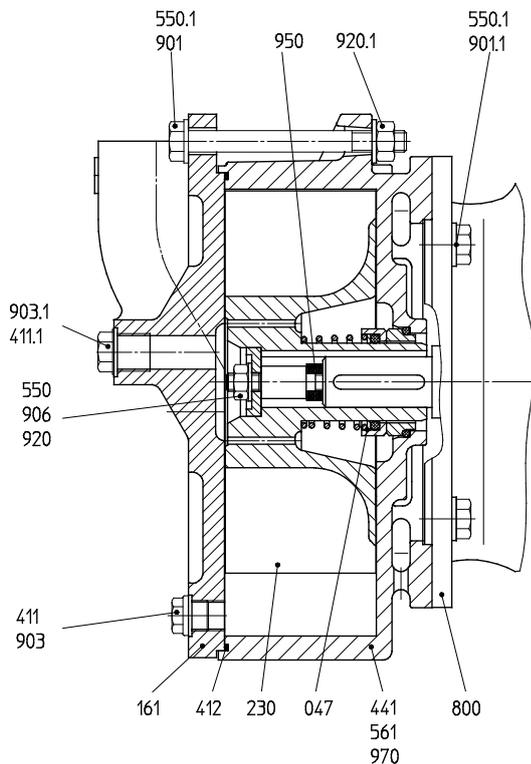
Schnittzeichnung VG-95/130/155 - Gewindeausführung
